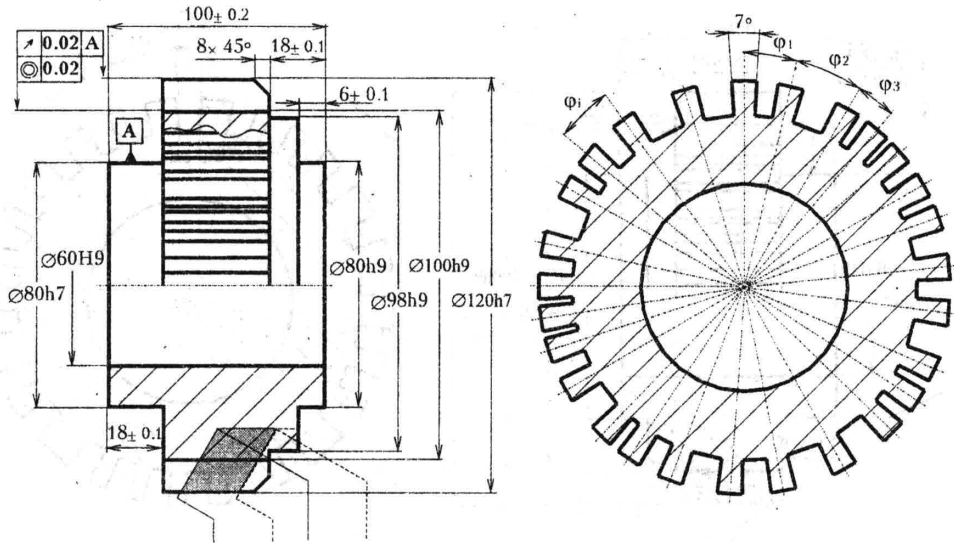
Креслення заготовки з однаковими радіальними виступами, відстань між якими є випадковою величиною
